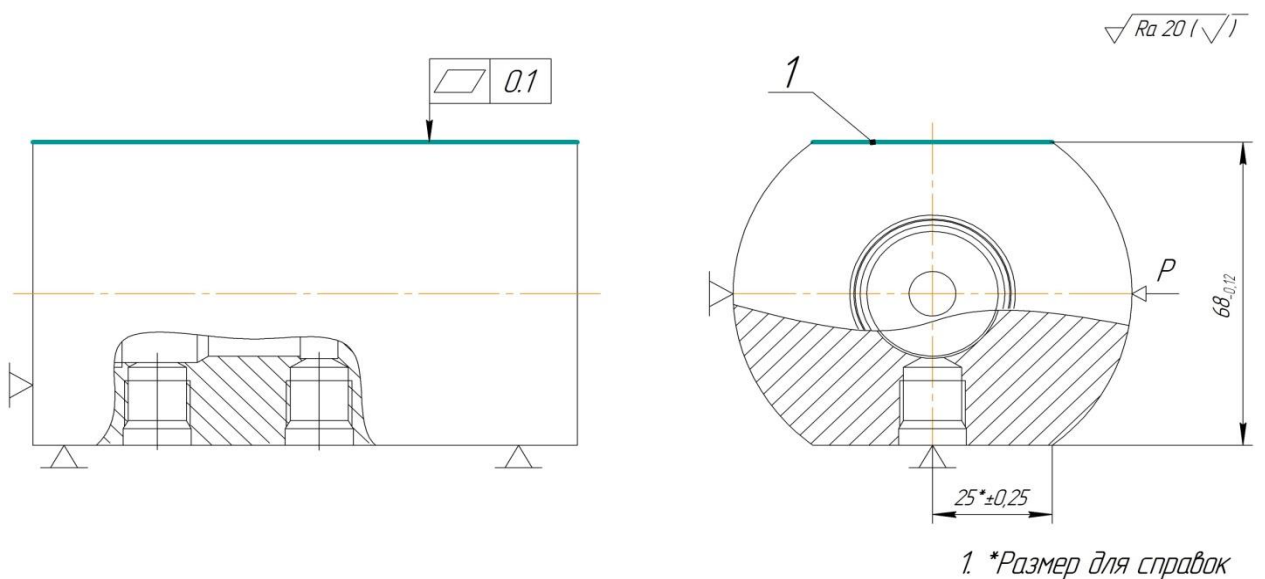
Операционный эскиз фрезерной обработки
